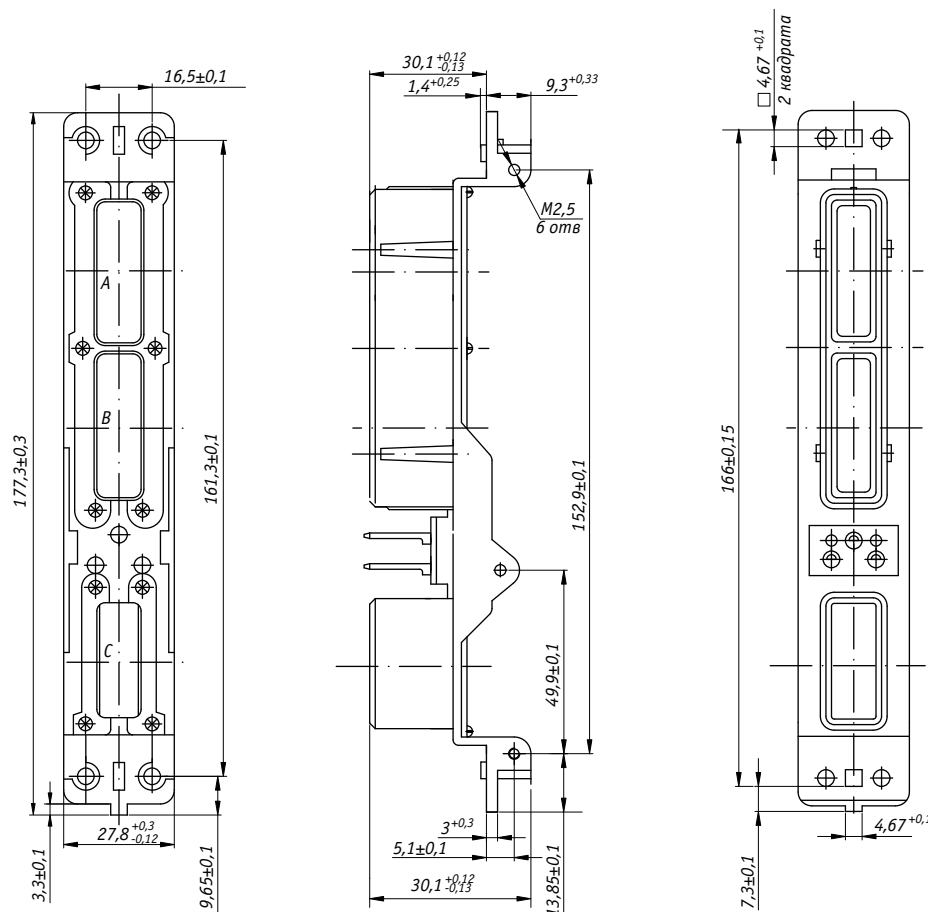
Корпус вилок ОКП-ВС-02-1В-101...
